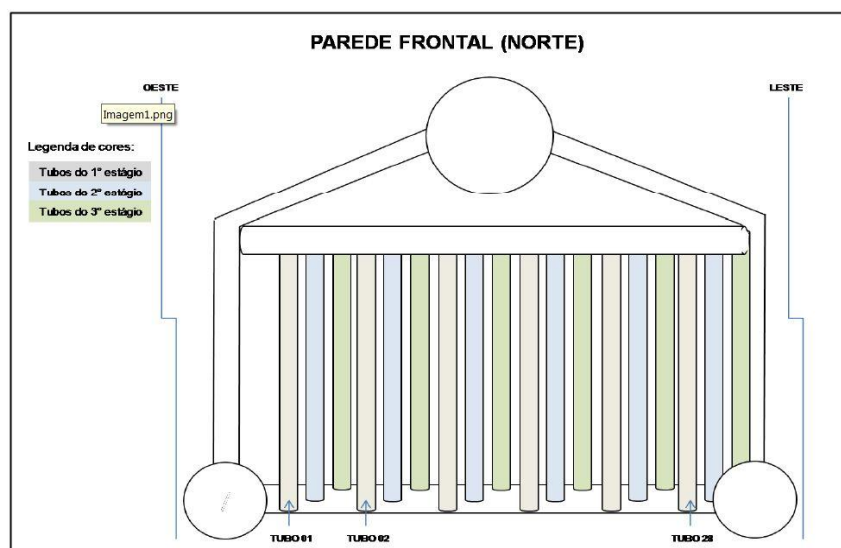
Vista detalhada da posição entre os tubos da face norte da caldeira. Fonte: Acinor (2010).
